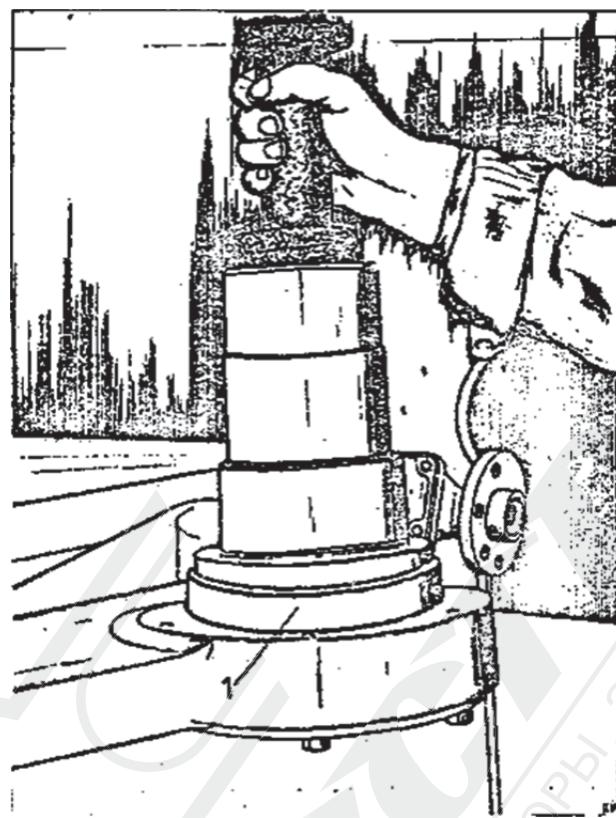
Запрессовка бочкообразного роликоподшипника в корпус с помощью стержня.
